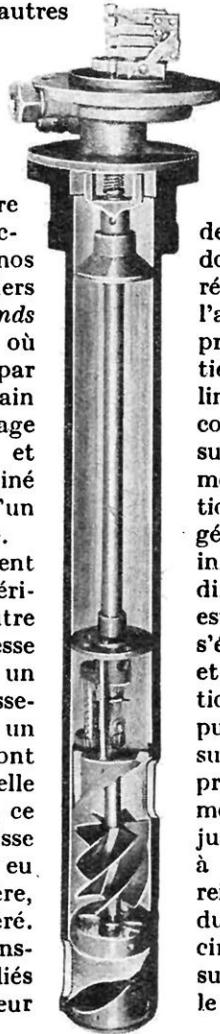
COUPE DE L'ÉLÉMENT TRANSMETTEUR DU LOCH
